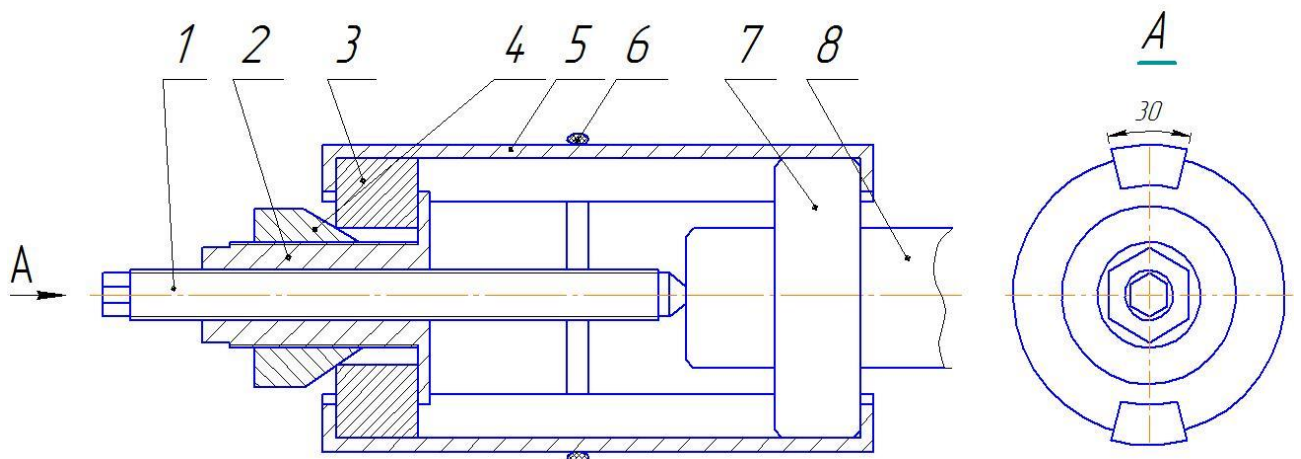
Знімач підшипників з симетричними лапами циліндричної форми: 1 – силовий гвинт; 2 – маточина; 3 – опора; 4 – конусна втулка; 5 – лапа; 6 – пружне кільце; 7 – підшипник; 8 – вал.
